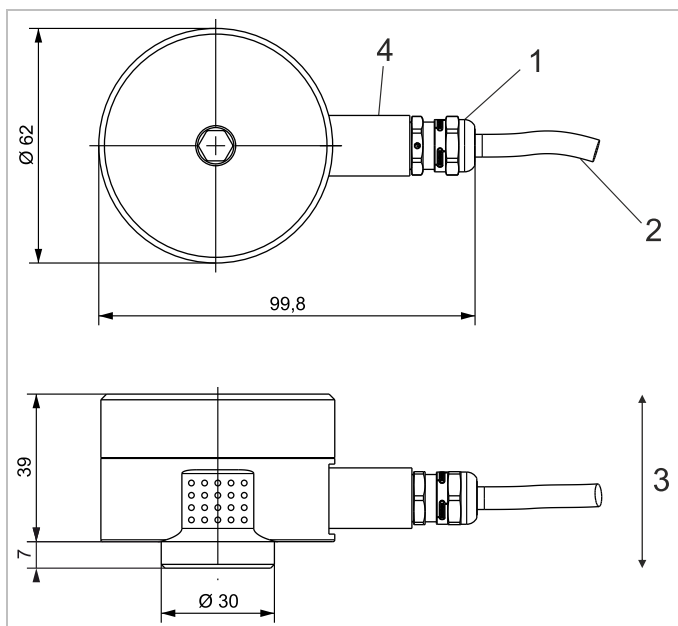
Boîtier avec câble intégré et base de manchon de serrage pour tuyau de protection métallique
